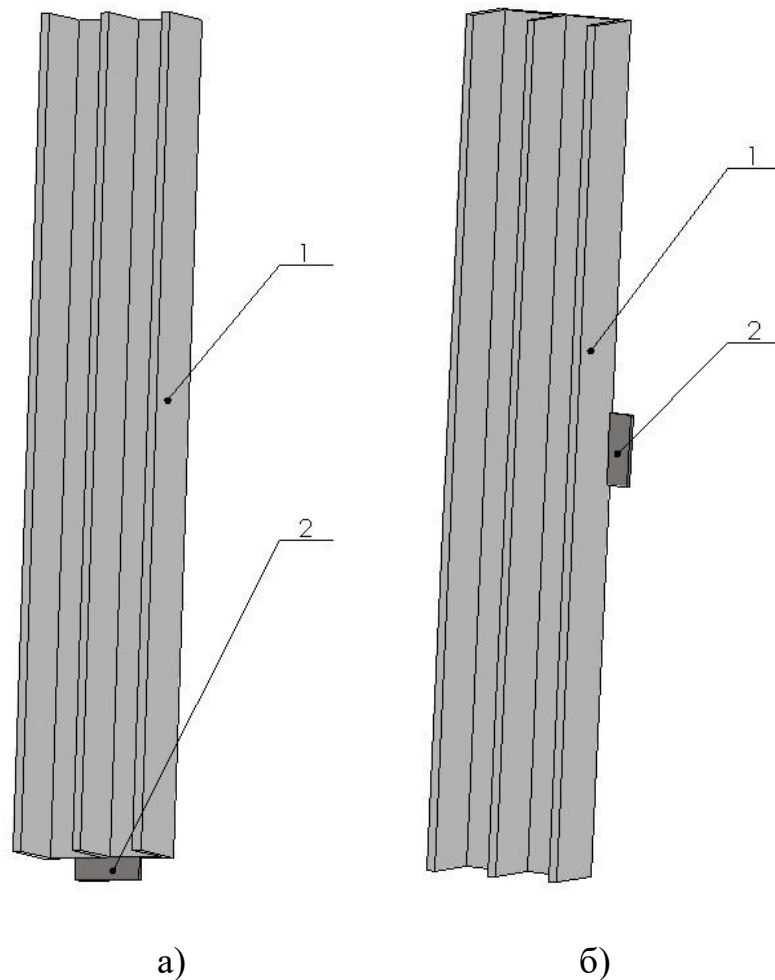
Отливка с питателем, 1 - отливка, 2 - питатель
